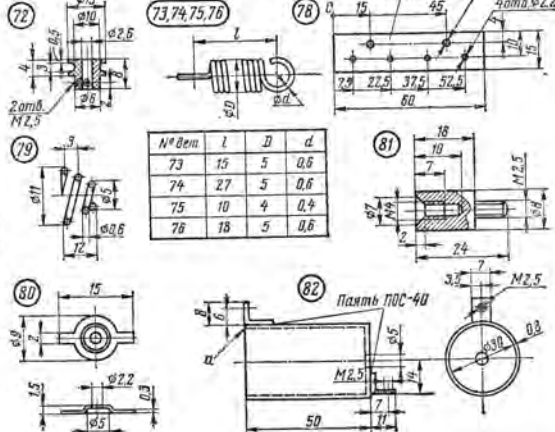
Детали лентопротяжного механизма: 72 — шкив электродвигателя, ЛС59-1, 1 шт; 73—76 — пружины, проволока стальная, по 1 шт; 78 — изоляционная пластина, гетинакс, 2 шт; 79 — пружина коническая, проволока стальная, 4 шт, закрепить с помощью заклепок 2×3 и деталей 80 на планках 78; 80 — контакт, Л62, 4 шт; 81 — стойка, Ст. А12, 1 шт; 82 — экран электродвигателя.
